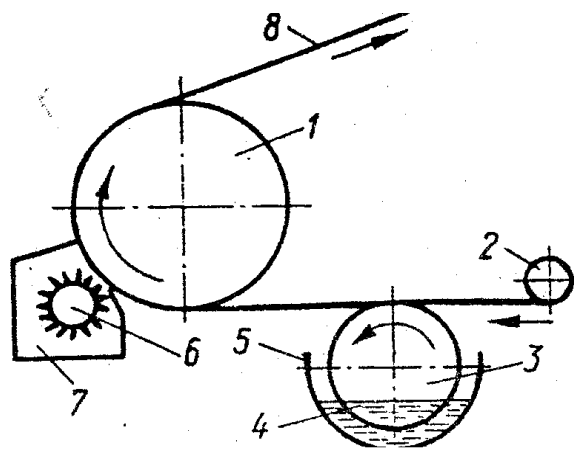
Схема устройства для нанесения покровного слоя с помощью вала и разравнивающей цилиндрической щетки:
